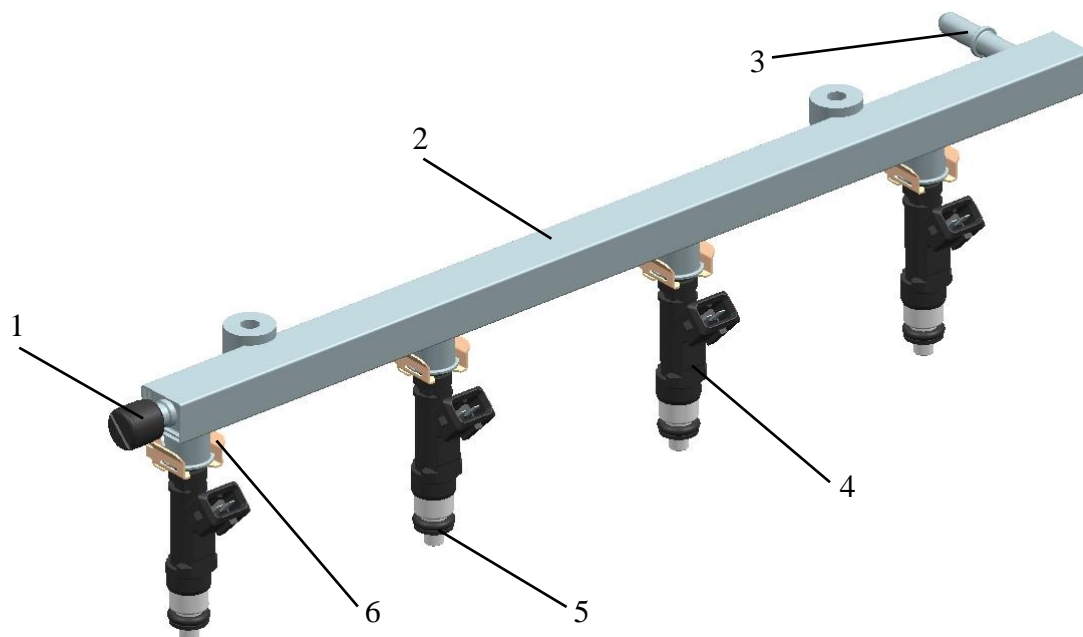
Топливопровод распределительный с форсунками 40904.1100010 и 40905.1100010:
